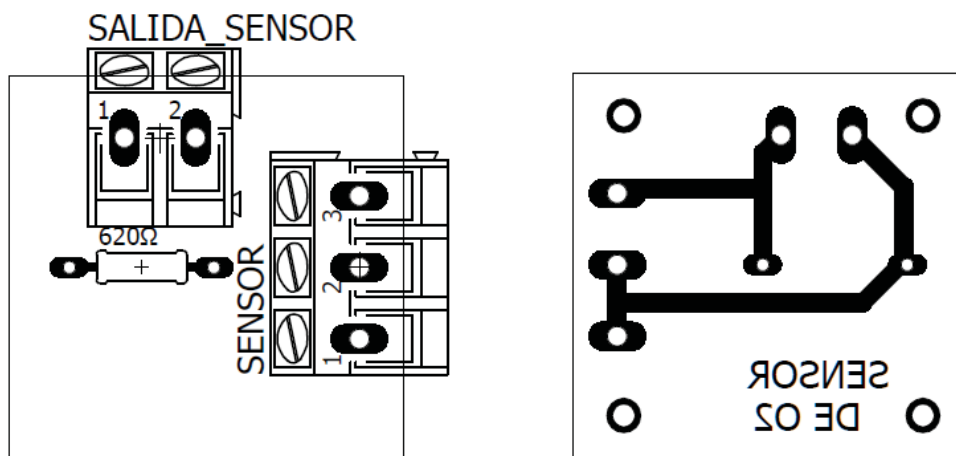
Diseño de la tarjeta de circuito impreso del sensor de oxígeno
